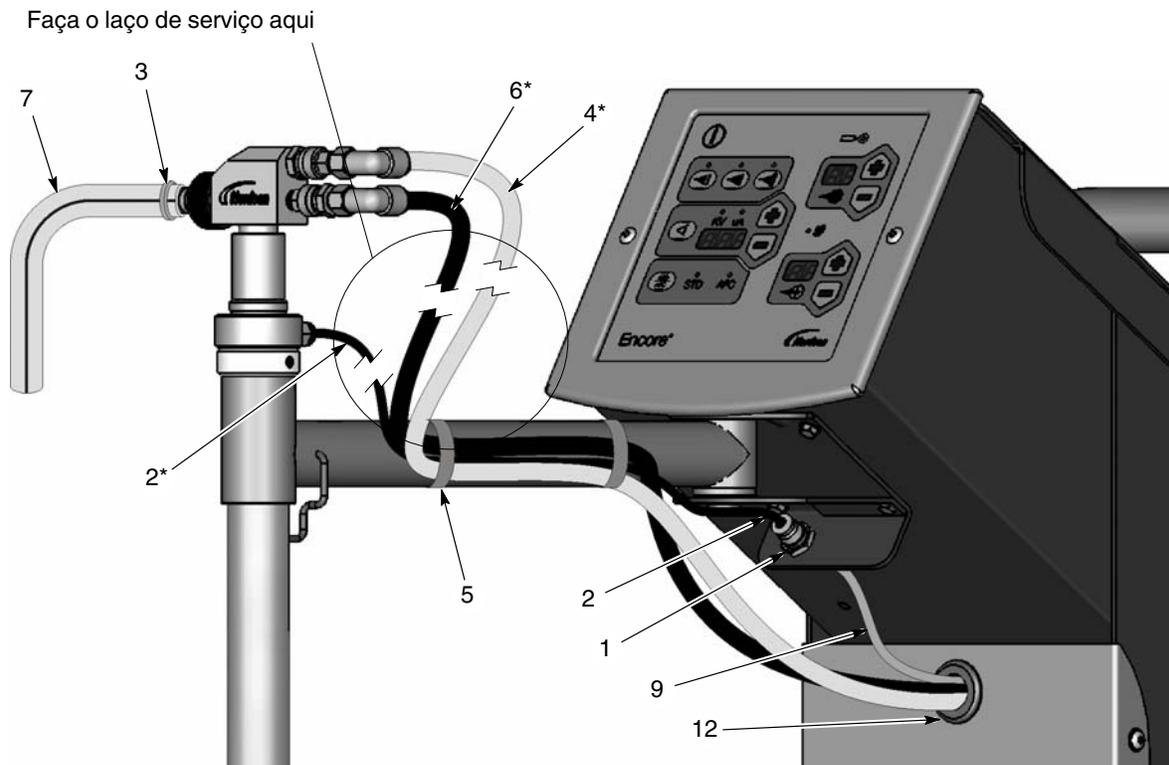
Tubo captador de pistola Encore LT e instalação da bomba
